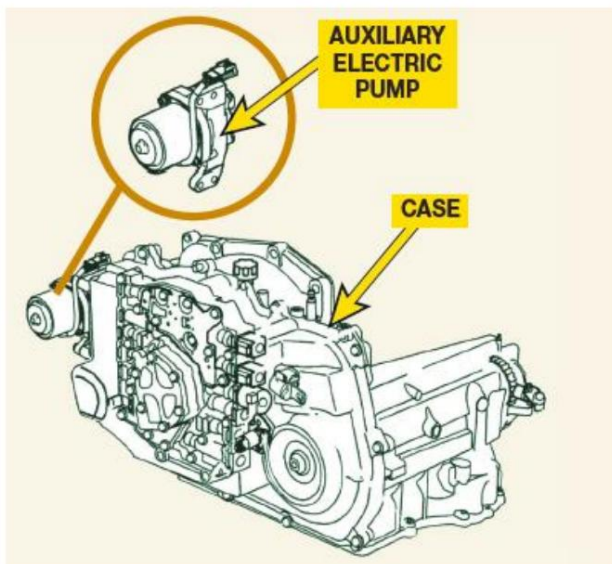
La bomba auxiliar mantiene la presión del fluido durante la parada del motor.
